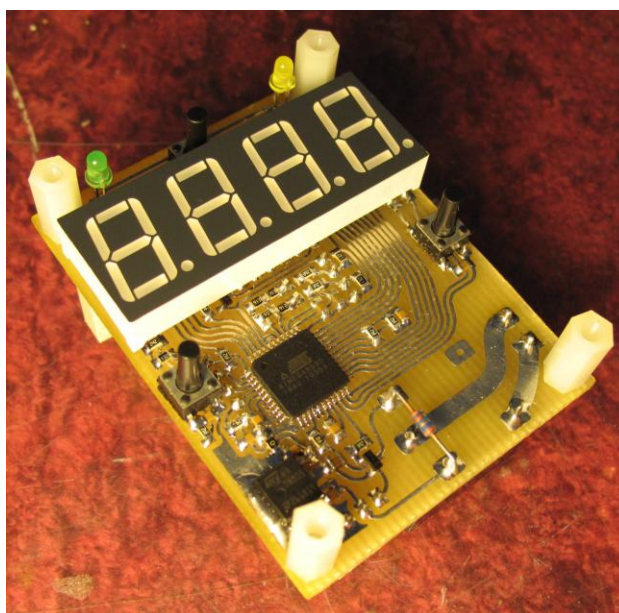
Цифровое управление сварочного аппарата Негуляева
